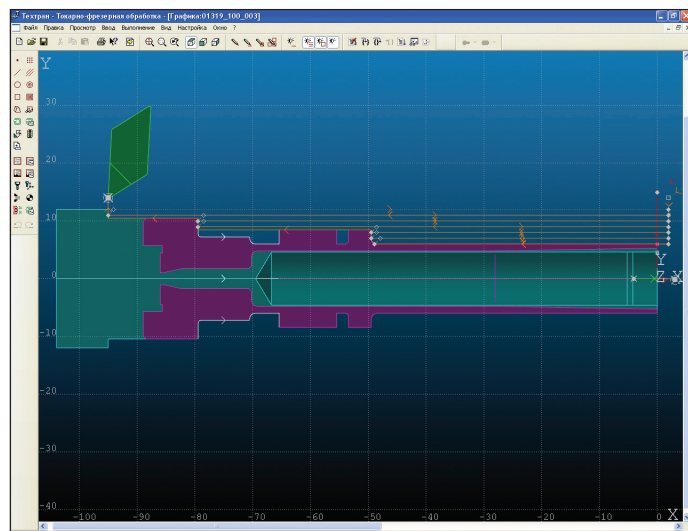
Представление токарной детали и заготовки в виде разреза (вид сбоку)
